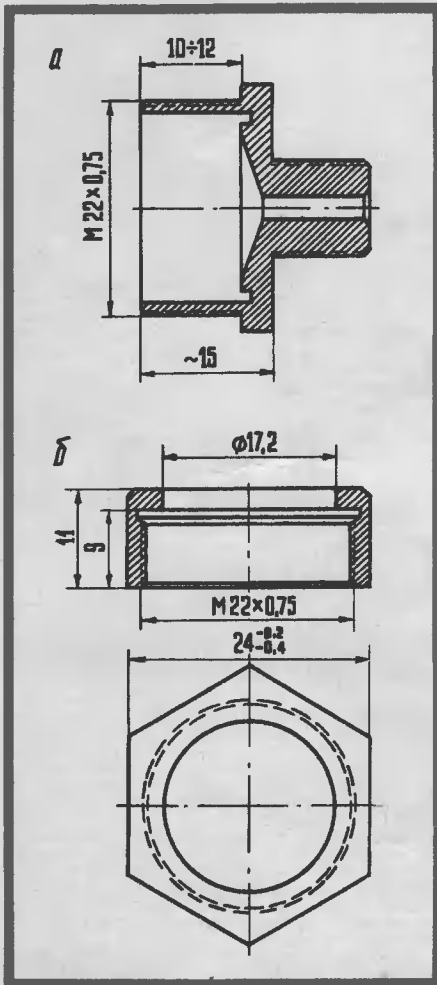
Детали выключателя: а — корпус; б — накидная гайка.
